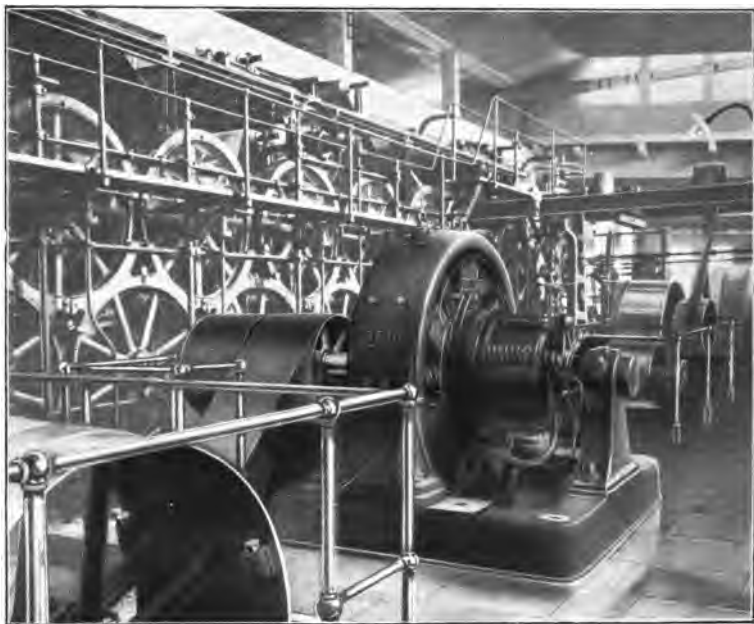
Motor 300 H. P. para máquina de fábrica papel.
